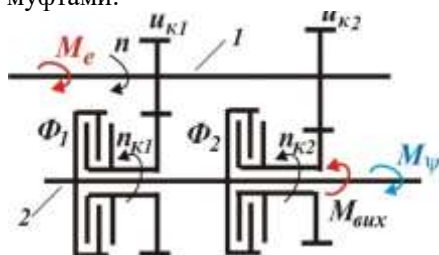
Фрагмент кінематичної схеми коробки передач:
